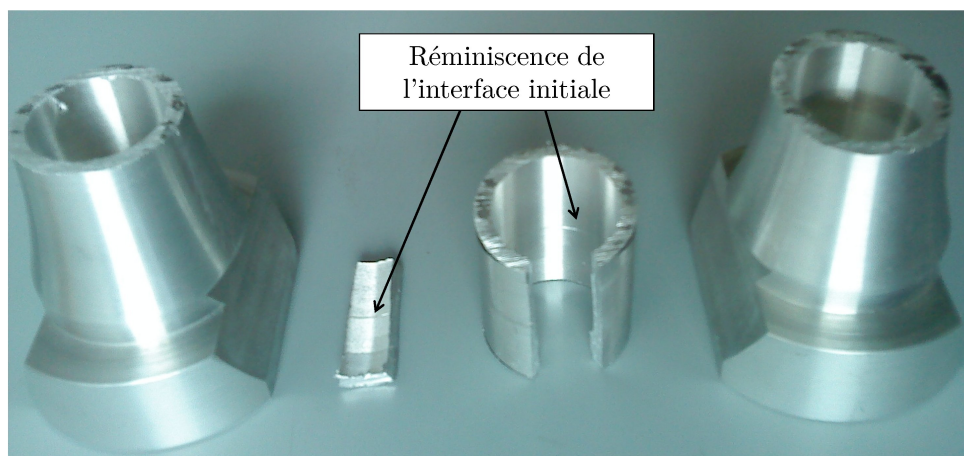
Photographie de la découpe d'une éprouvette soudée (essai 10). La ligne à mi-hauteur sur les parties découpées est une réminiscence de l'interface initiale.
